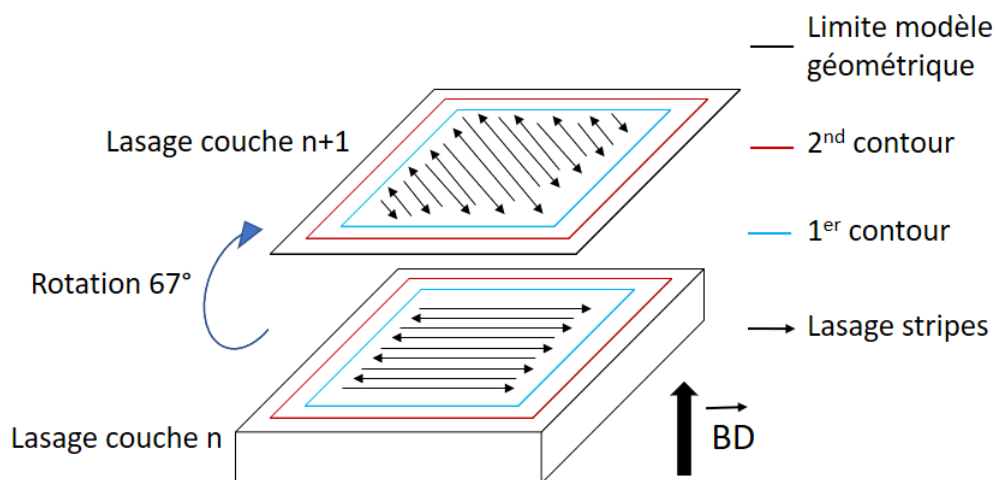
Stratégie de lasage utilisée pour la fabrication des éprouvettes SLM.
